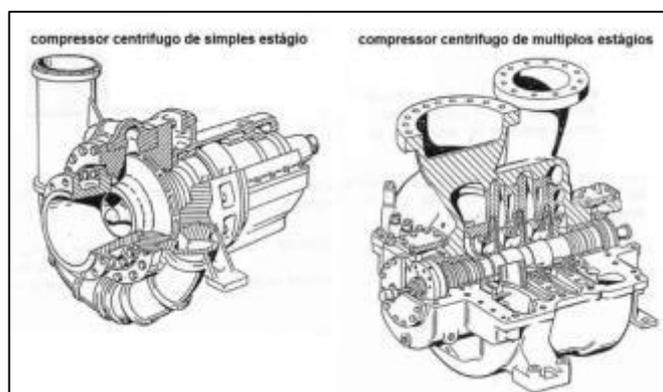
Detalhe de compressor centrífugo de simples e múltiplos estágios.
